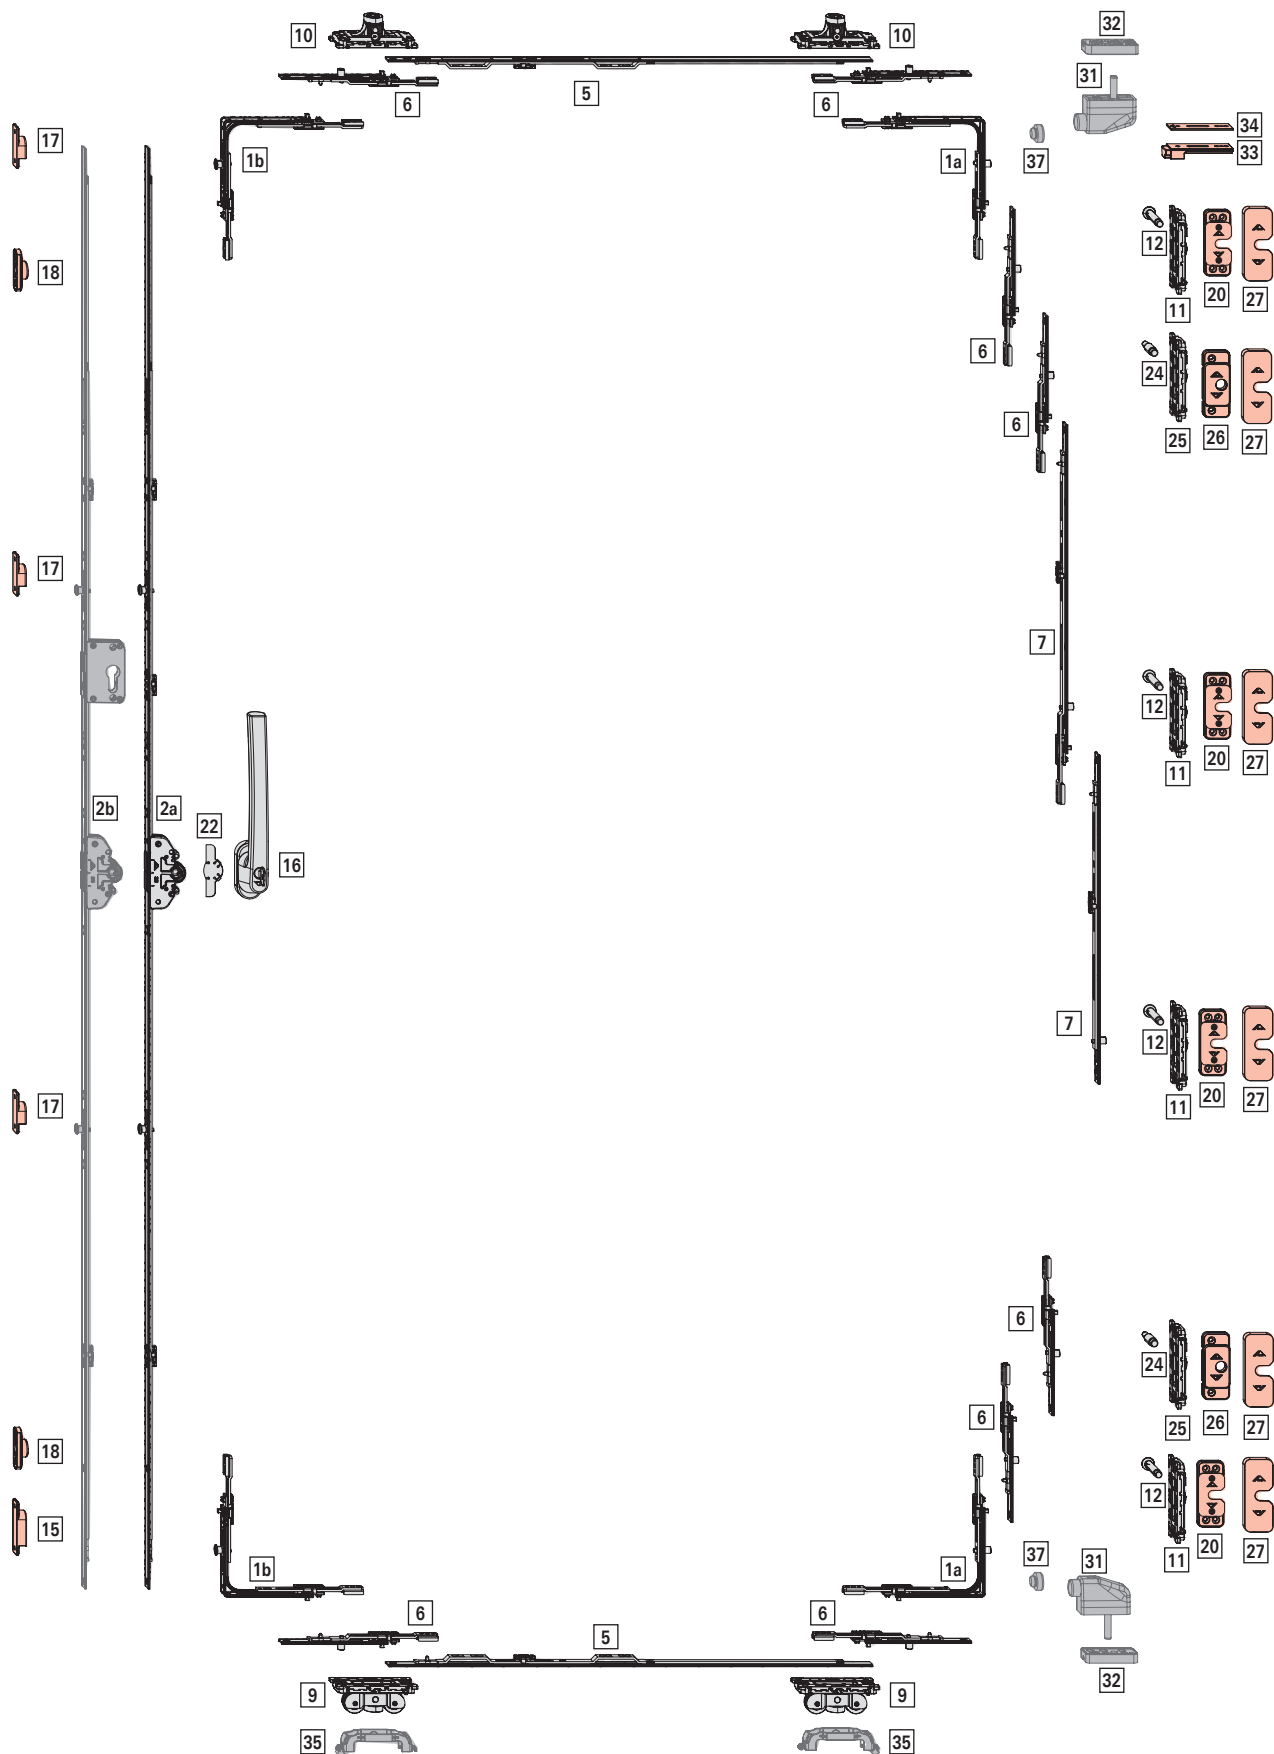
abgebildet: Kunststoff; Ausführung DIN links; FFB 900 mm; FFH 1800 mm; Getriebe DM 35
